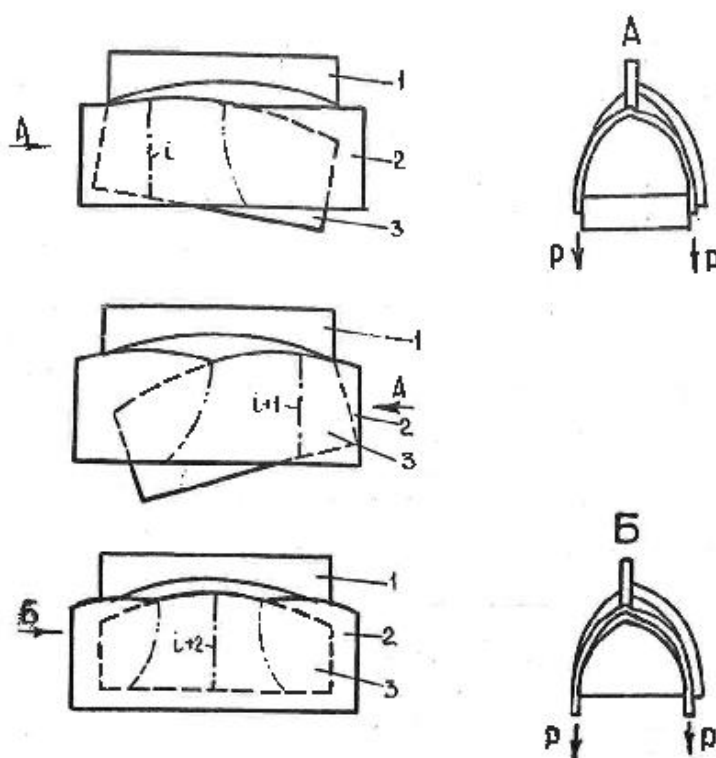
Последовательное растяжение заготовки: 1 - заготовка; 2 - пуансон; 3 – шаблон
